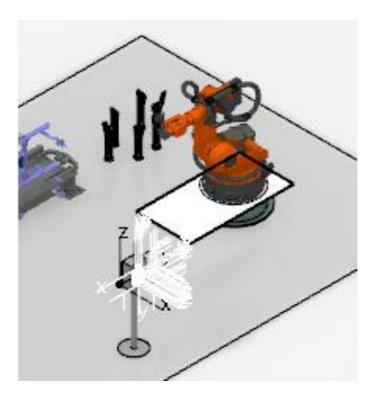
Posicionamiento de recursos en la planta mediante DELMIA Plant Layout Design.
